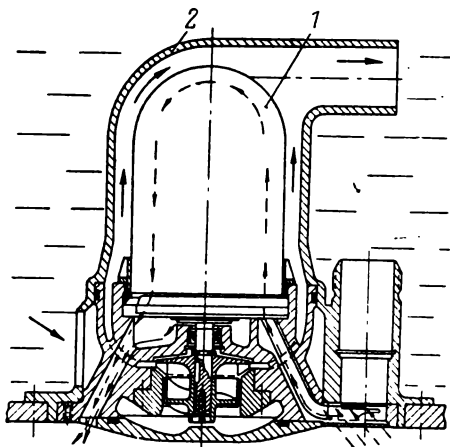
Кессонный ЭЦН с верхним расположением рабочего колеса:
